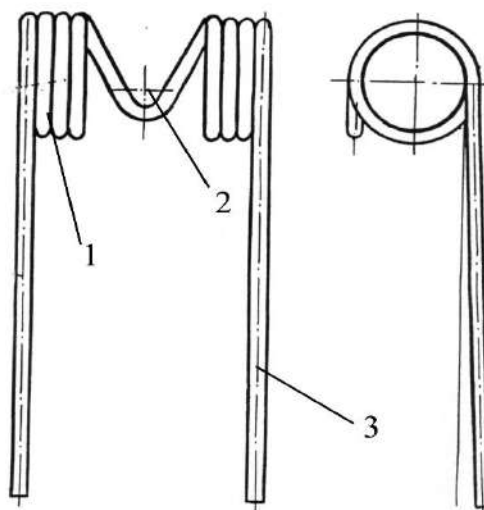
Спарені пружинні зуби з циліндричними пружинами кручення:
